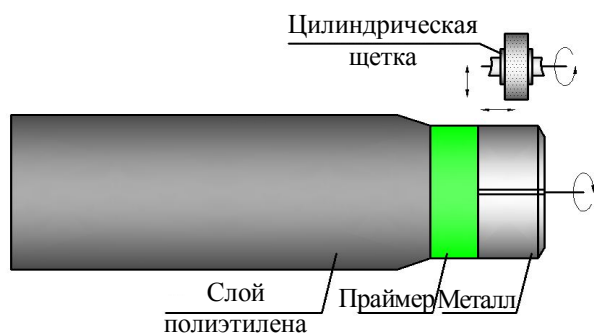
Схема обработки цилиндрической щеткой края трубы
